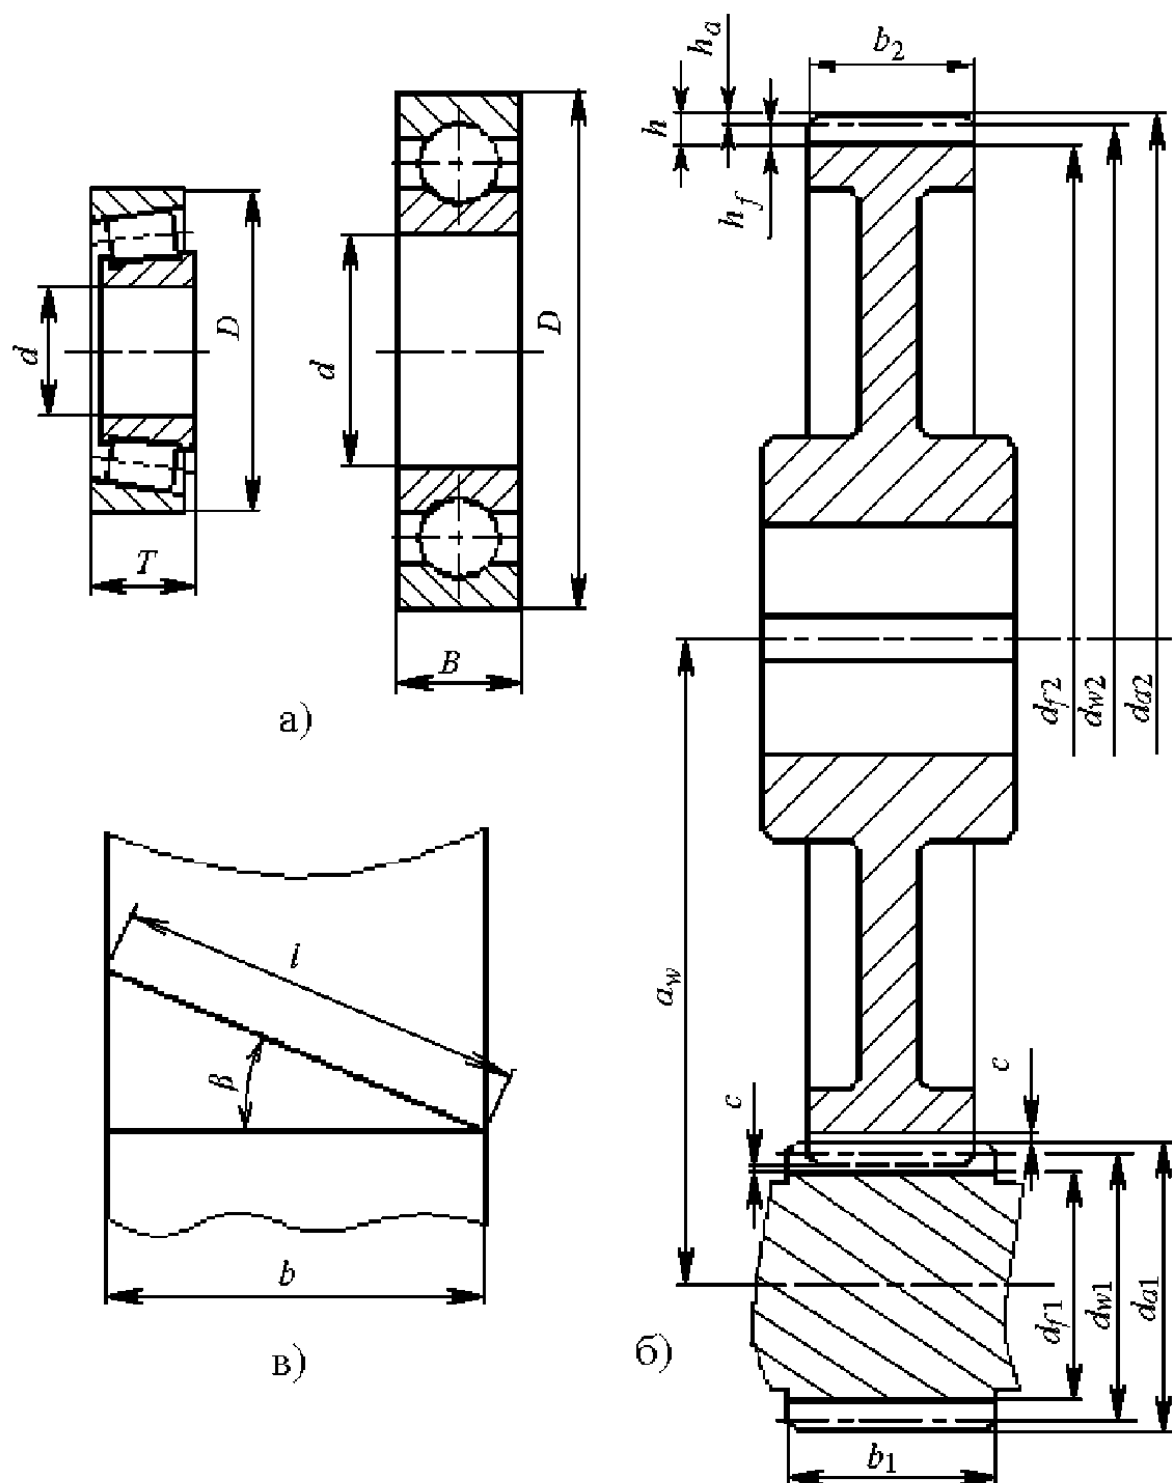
Параметры подшипников и зубчатого зацепления
